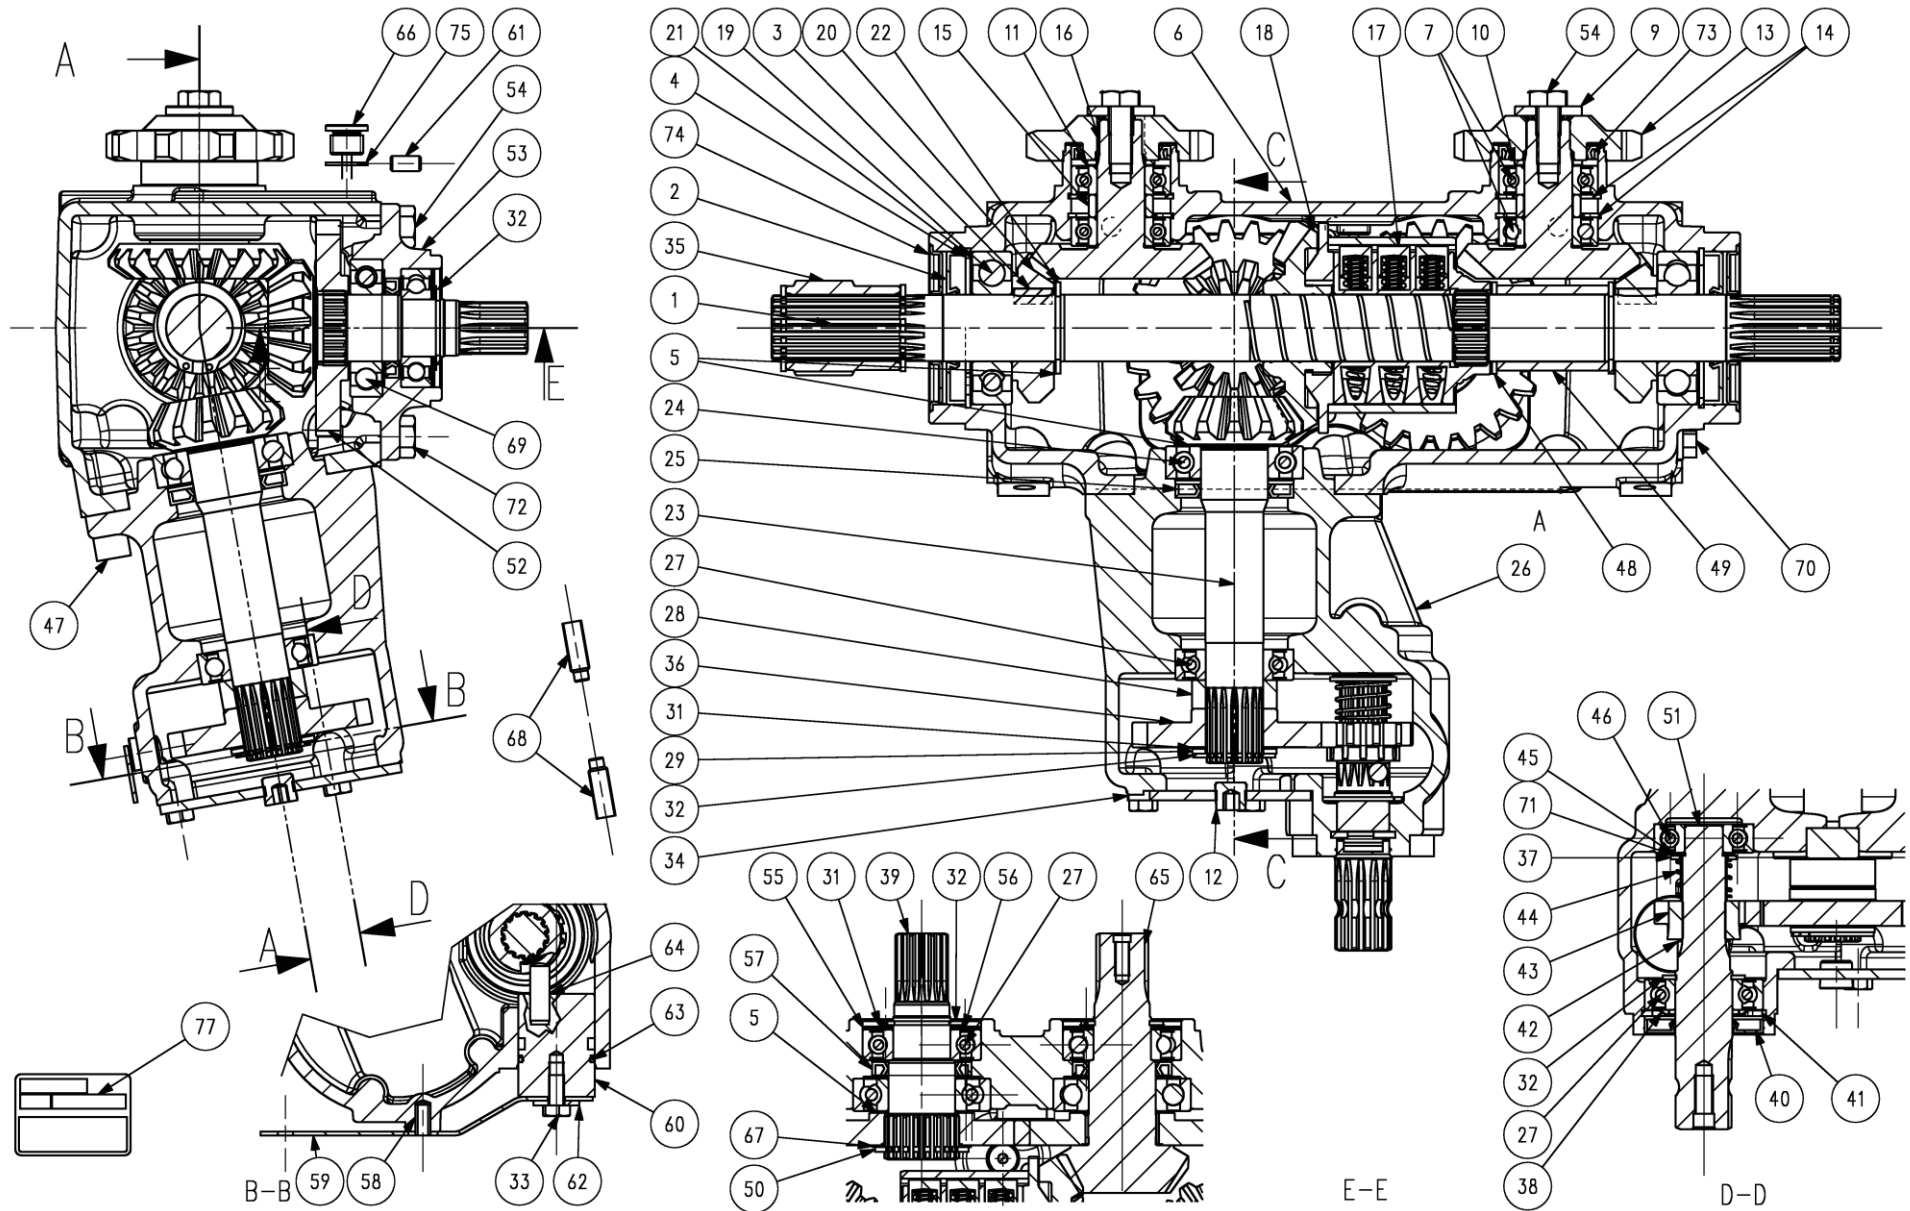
Редуктор русла левый 9.170.162.10 "Comer industries"
